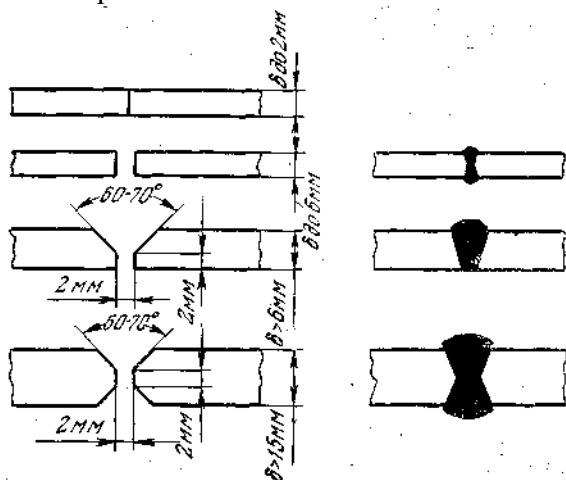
Виды кромок, подготовленных под сварку
